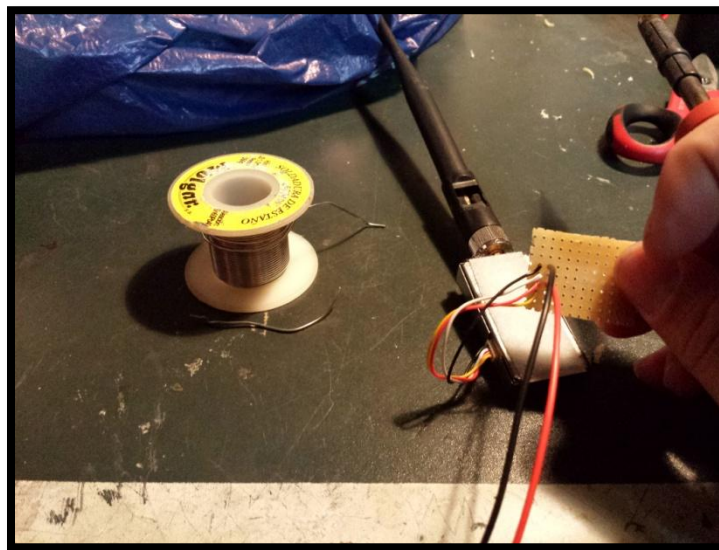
Soldadura a la placa del conector JST.
